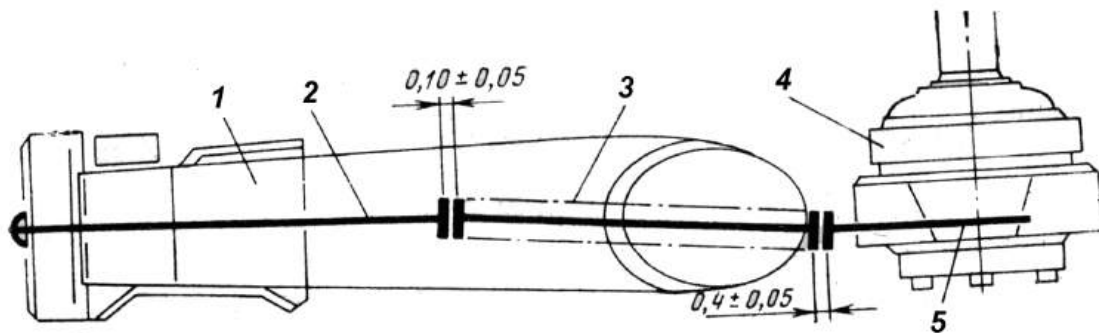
Схема регулювання положення двигунів відносно редуктора на вертольоті:
